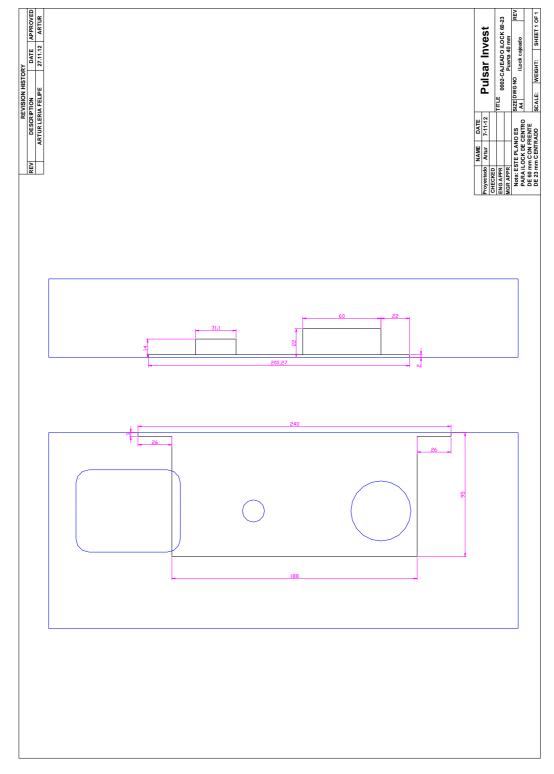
Cajeado de la cerradura iLock para una puerta de 40 mm de grueso.
